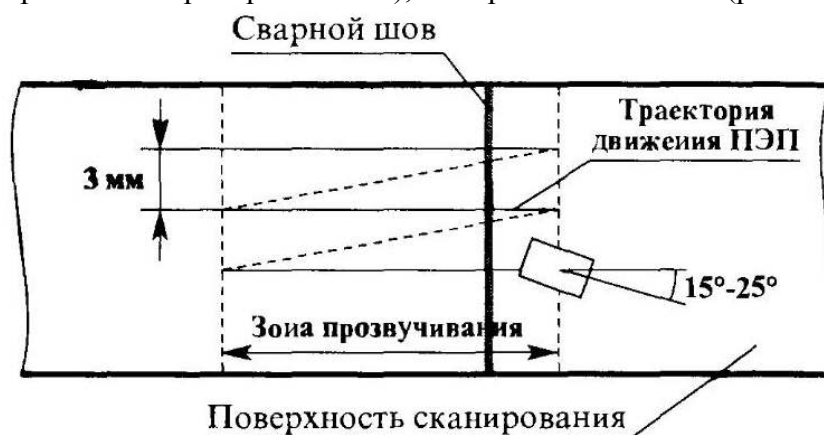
Схема движения преобразователя по поверхности сканирования в пределах зоны прозвучивания при контроле сварного стыка
